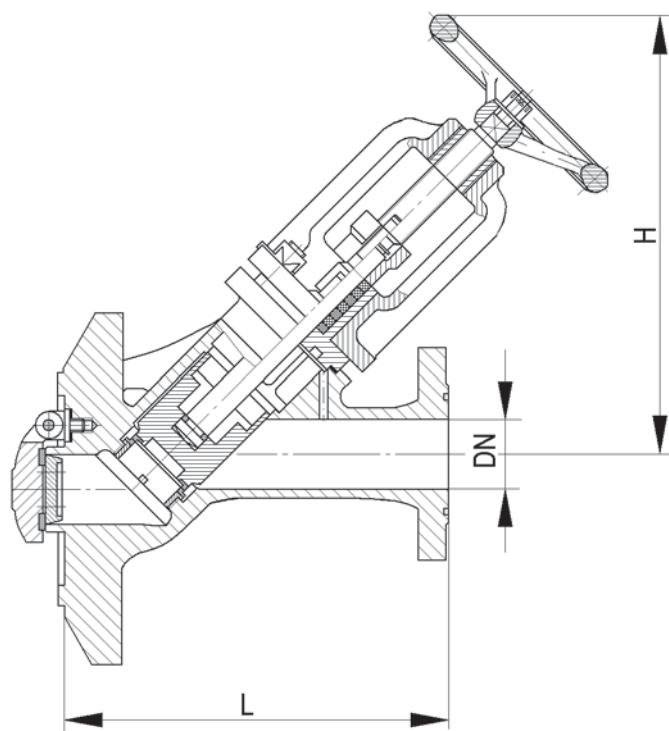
Клапан бортовой запорный прямооточный с захлопкой
